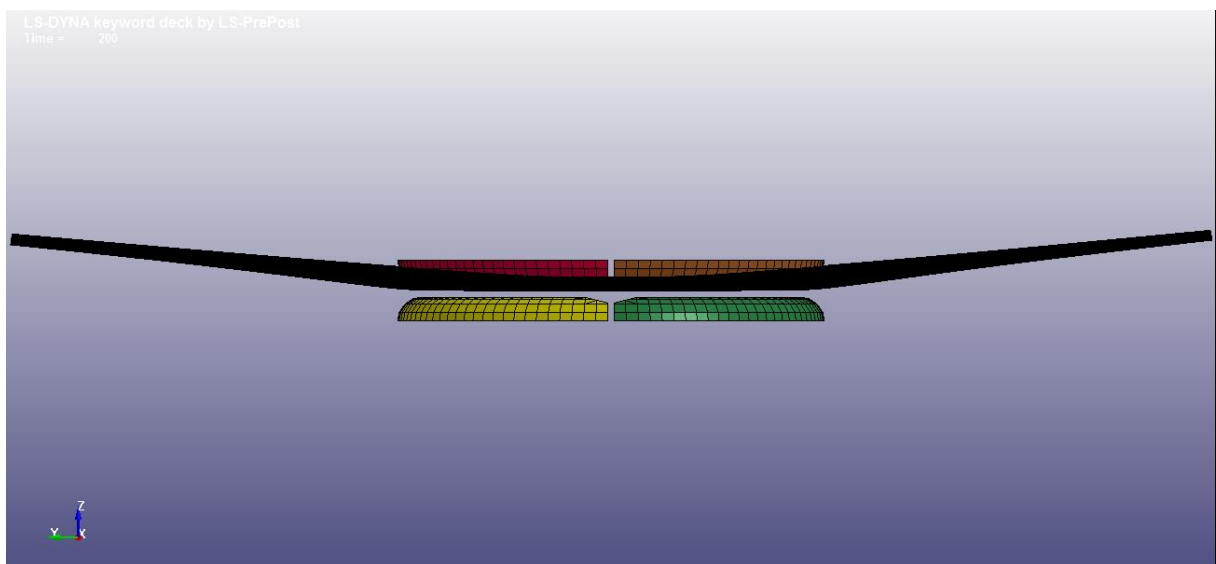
entstandene Blechgeometrie, nachdem sich die Werkzeugbacken wieder in ihrer Ausgangsposition befinden (Frontansicht)
